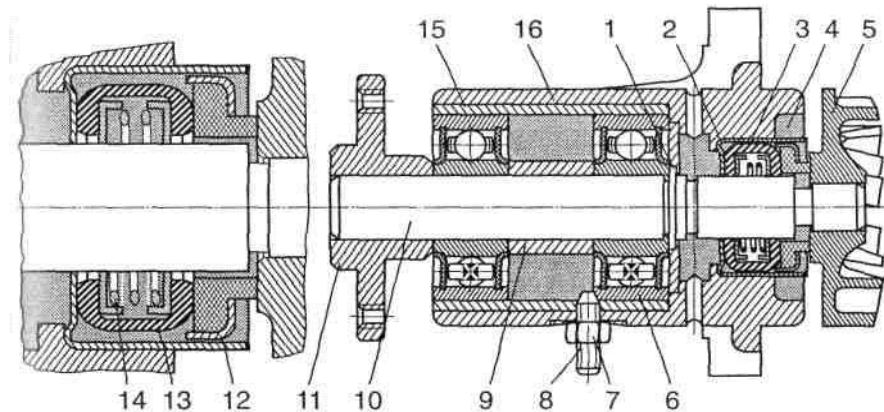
Водяний насос: 1 - стопорне кільце; 2 - корпус ущільнювача; 3 - манжета; 4 - ущільнювальна шайба; 5 - крильчатка; 6 - підшипник; 7 - контргайка; 8 - стопорний гвинт підшипника; 9 - розпірна втулка; 10 - вал; 11 - маточина; 12 - корпус ущільнювальної шайби; 13 - обойма; 14 - пружина; 15 - стакан підшипників; 16 - корпус насоса
